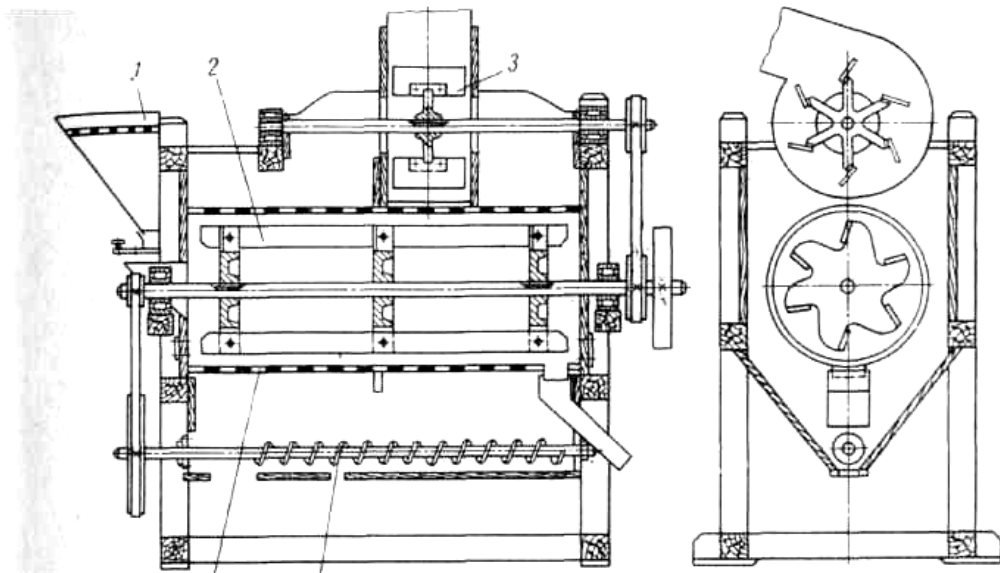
Схема скарифкатора СВВ-0,2: 1 – засипний ківш; 2 – бильний барабан; 3 – вентилятор; 4 – шнек; 5 – обичайка
